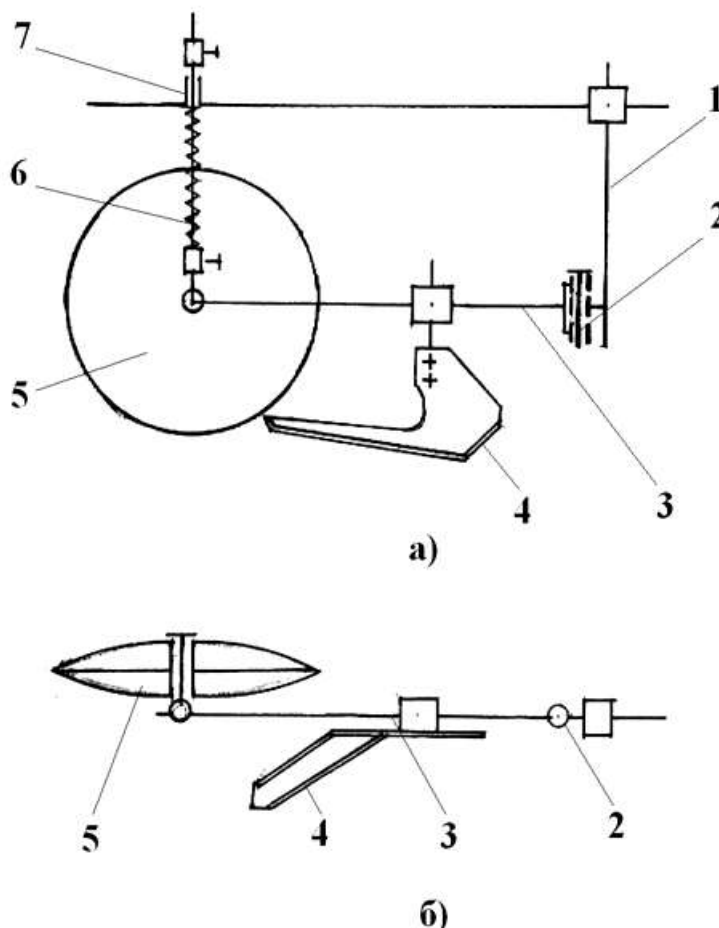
Стабилизирующий рабочий орган культиватора; вид с боку (а) и вид сверху (б):
